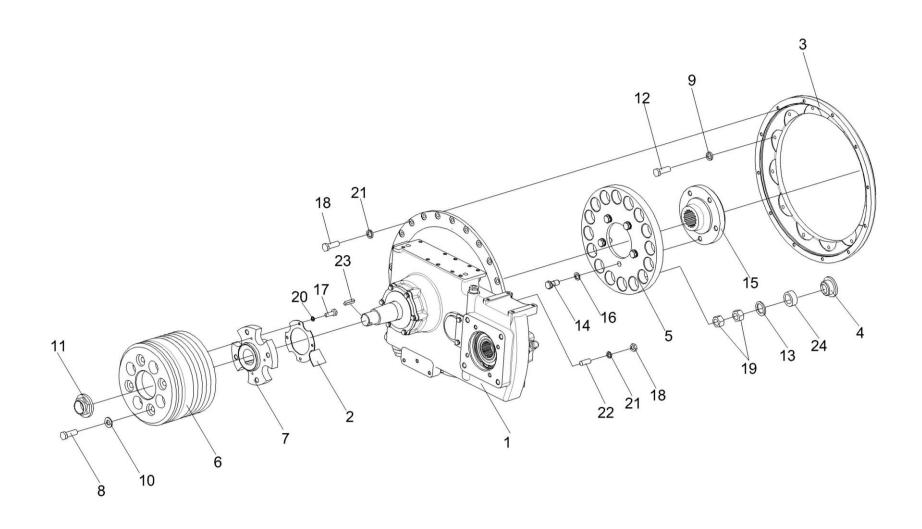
Установка главного привода КЗК-10-1-0106030-02
